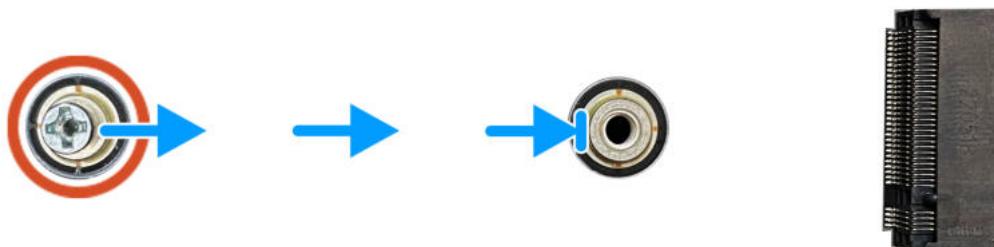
Schraubbefestigung für Solid-State-Laufwerk
